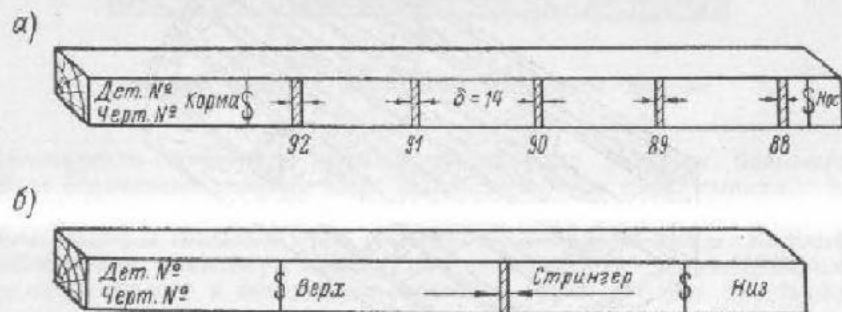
Рейки для разметки: а — продольная рейка; б — поперечная рейка.
